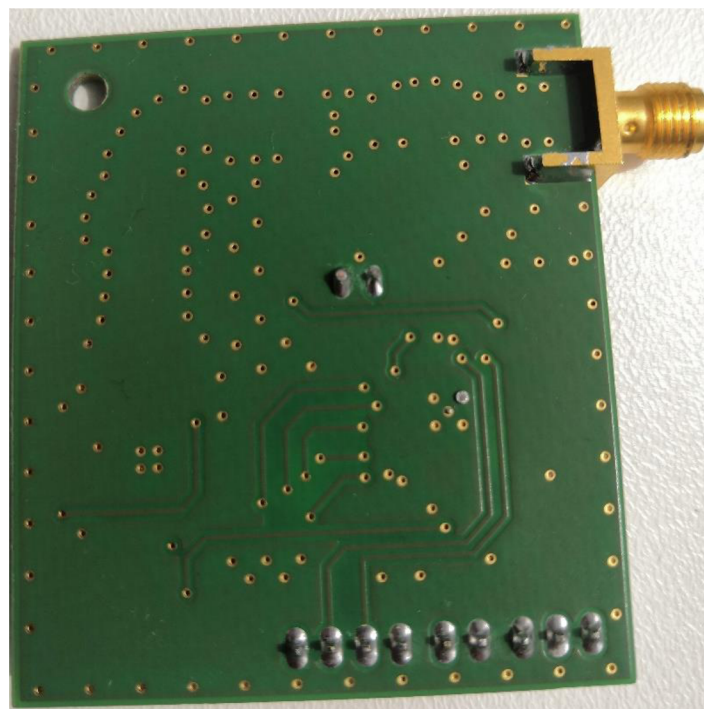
Deska plošného spoje – vrstva BOTTOM
